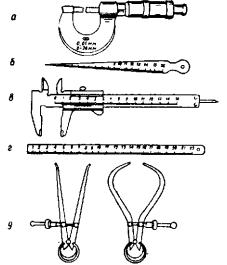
Измерительные инструменты: а — микрометр; б —нутромер; в —штангенциркуль; г—измерительная линейка; д—кронциркули.
